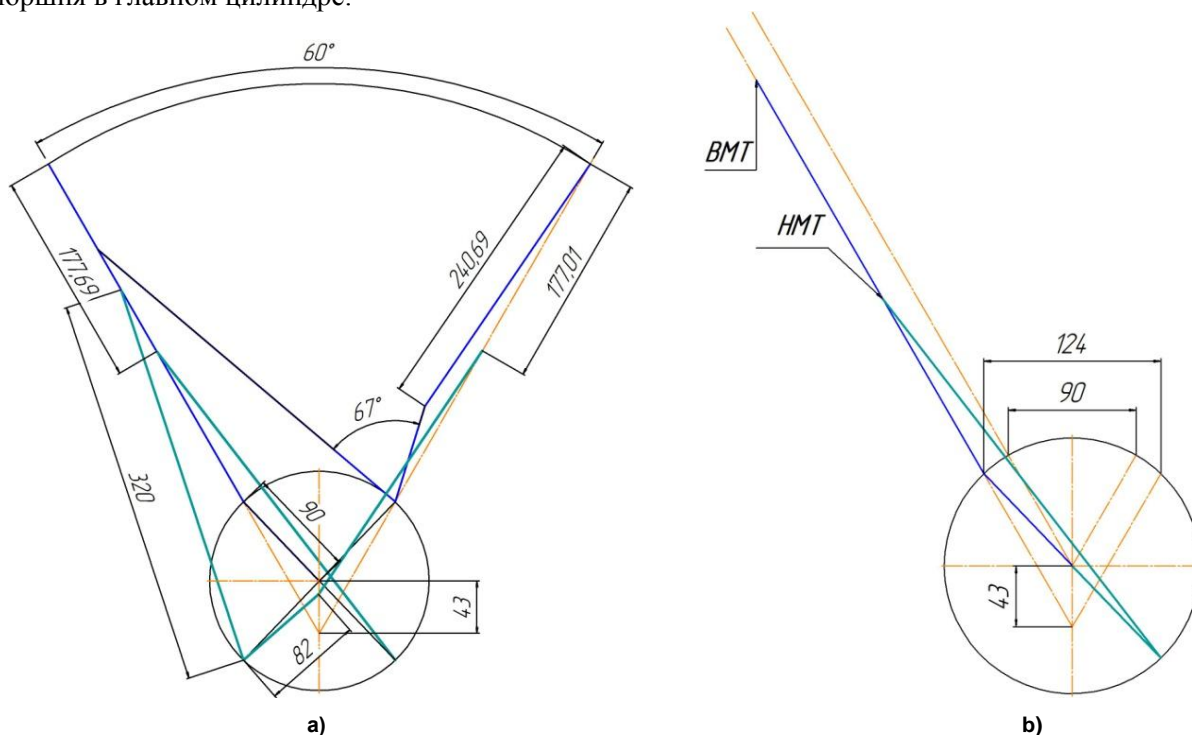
Кинематическая схема формирования одинакового хода поршней при смещении осей цилиндров двигателя
